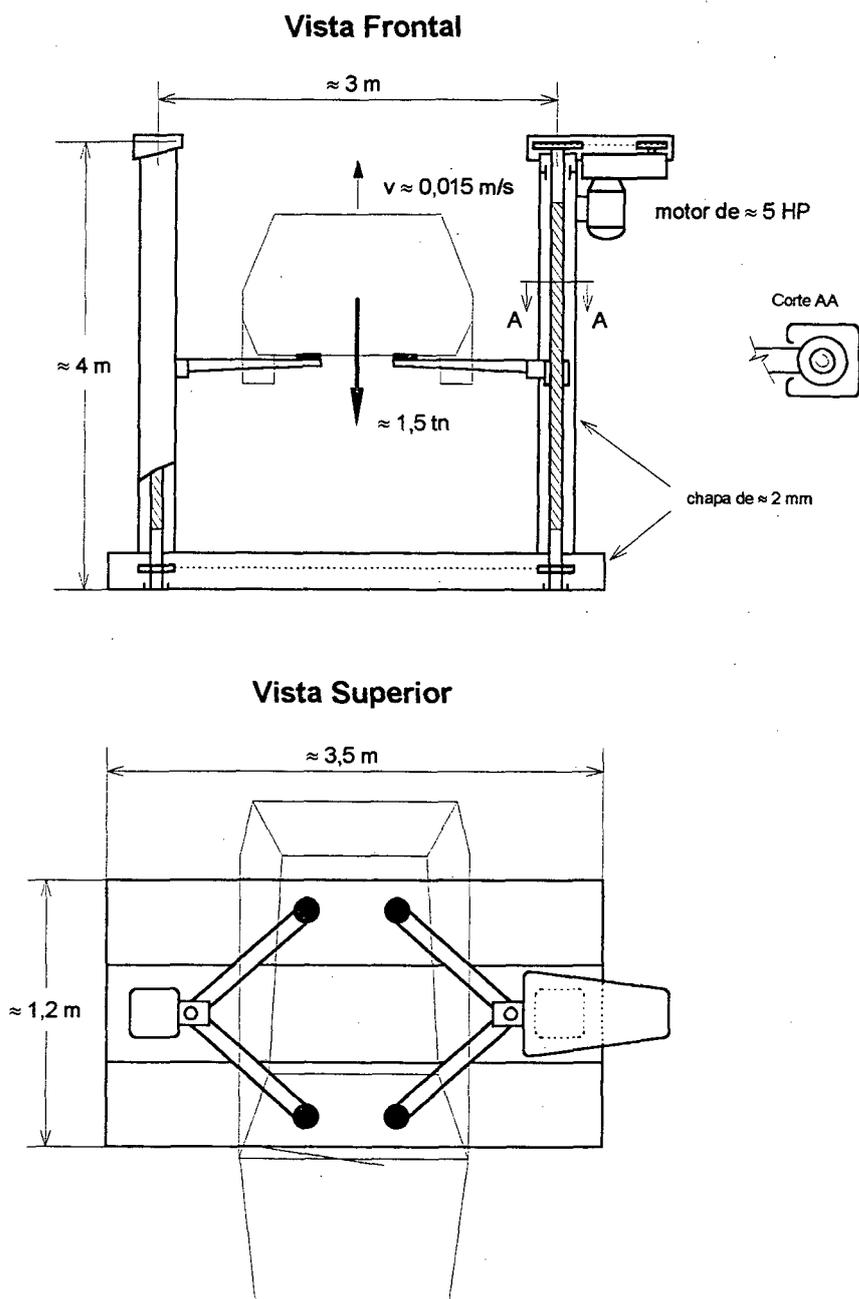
11 Modelo de concepção para um elevador de automóveis.
